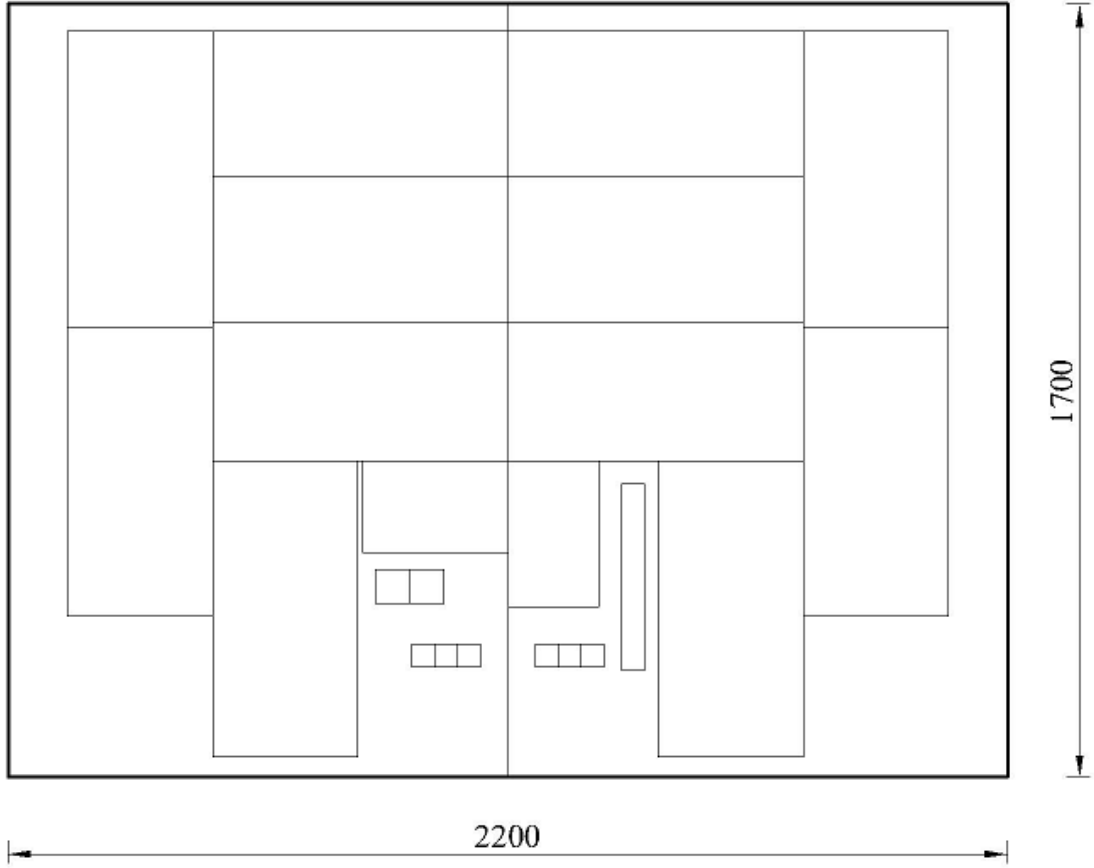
16 mm Yonga levha Kesim Planı (ölçüler mm)
